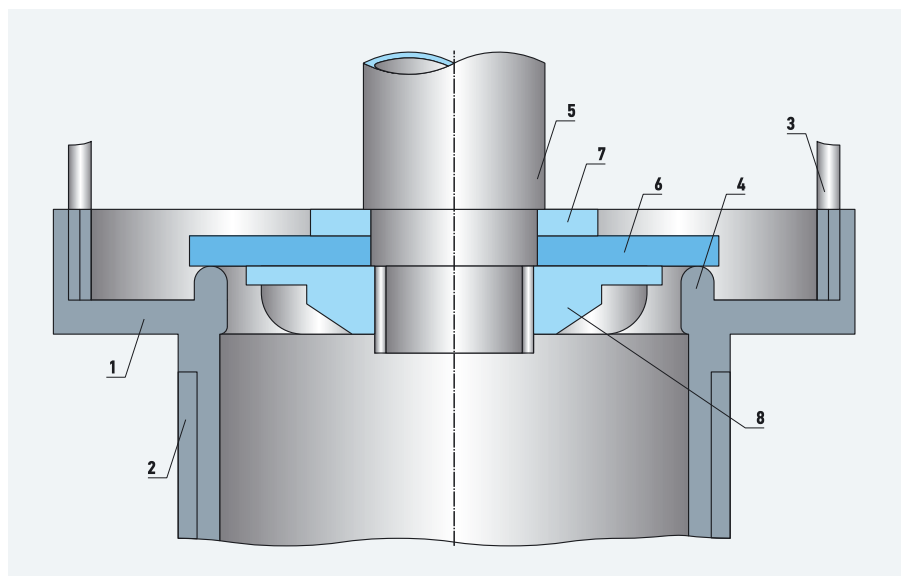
Спускной клапан с устройством, имитирующим коноидальный насадок (1 — опорное кольцо корпуса; 2 — нижняя часть корпуса; 3 — верхняя часть корпуса; 4 — седло; 5 — переливная труба; 6 — плоский эластичный клапан; 7 — опорное кольцо клапана; 8 — крепежная гайка)
